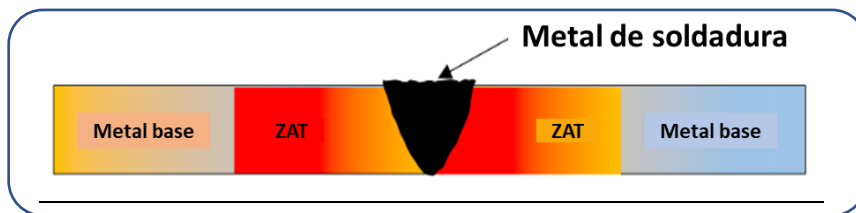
Perfil de la soldadura que muestra MB, HAZ y MS.
